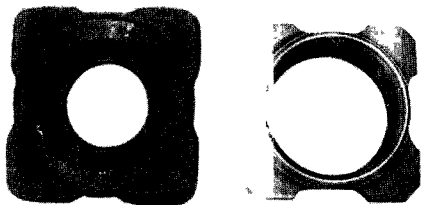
Заготовка корпуса втулки четырехлопастного винта
